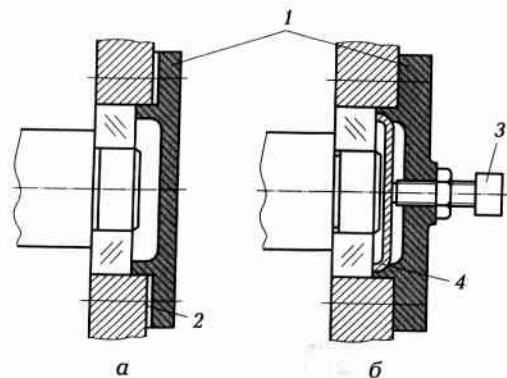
Схемы стопорения подшипников крышкой (а) и болтом (б): 1 — крышка; 2 — прокладка; 3 — болт; 4 — шайба
